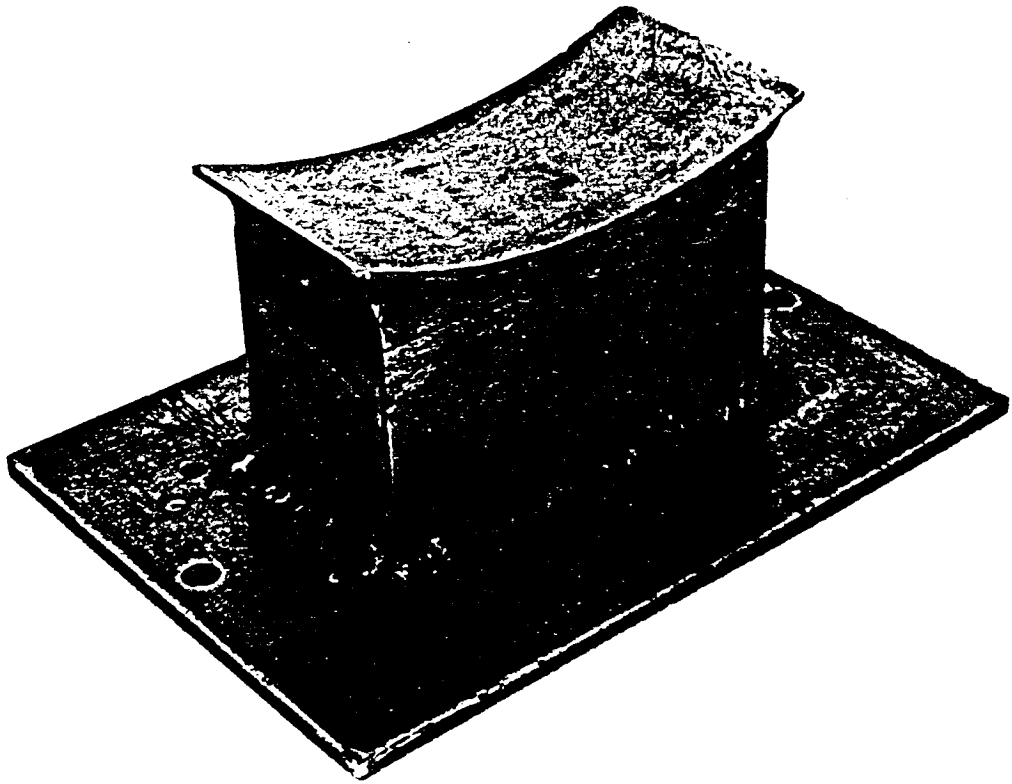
Parte inferior do molde correspondente à seção da parede externa do cilindro soldada sobre a câmara de refrigeração.
